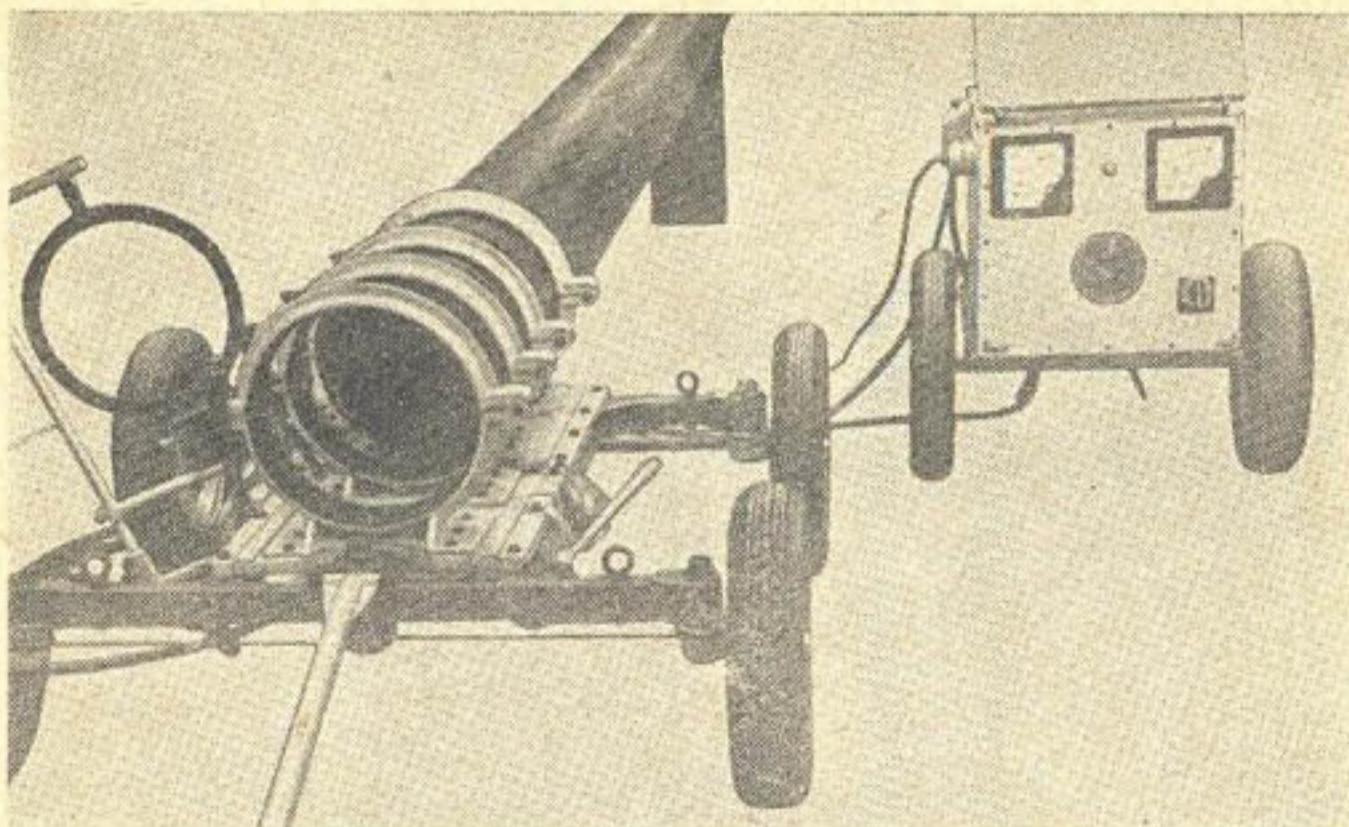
Установка для сварки полиэтиленовых труб встык.
